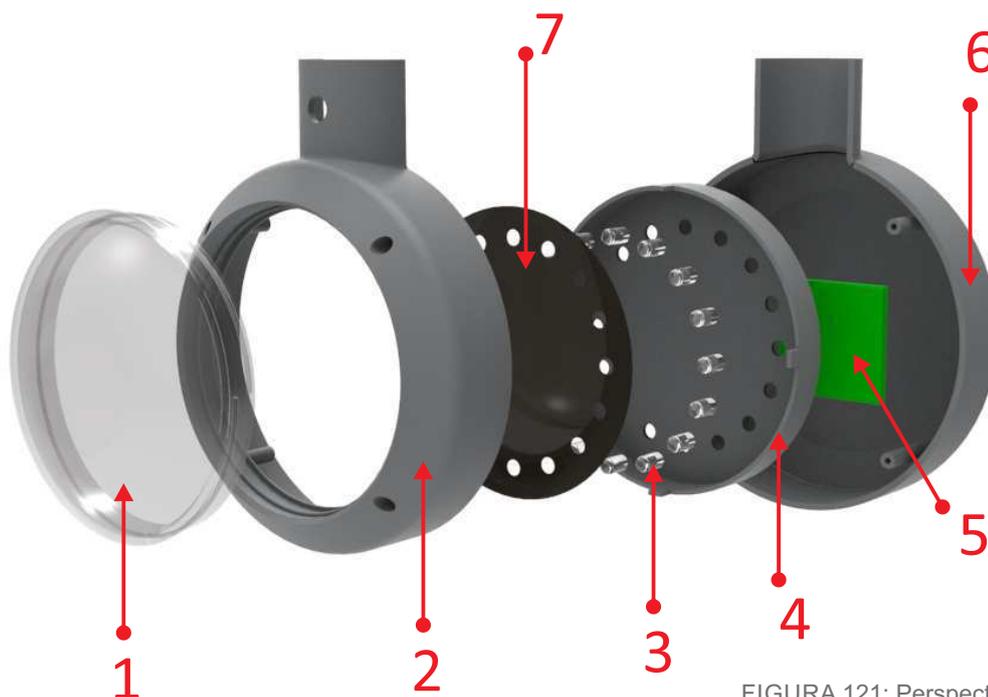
Perspectiva explodida da carenagem maior de 1 conexão.
